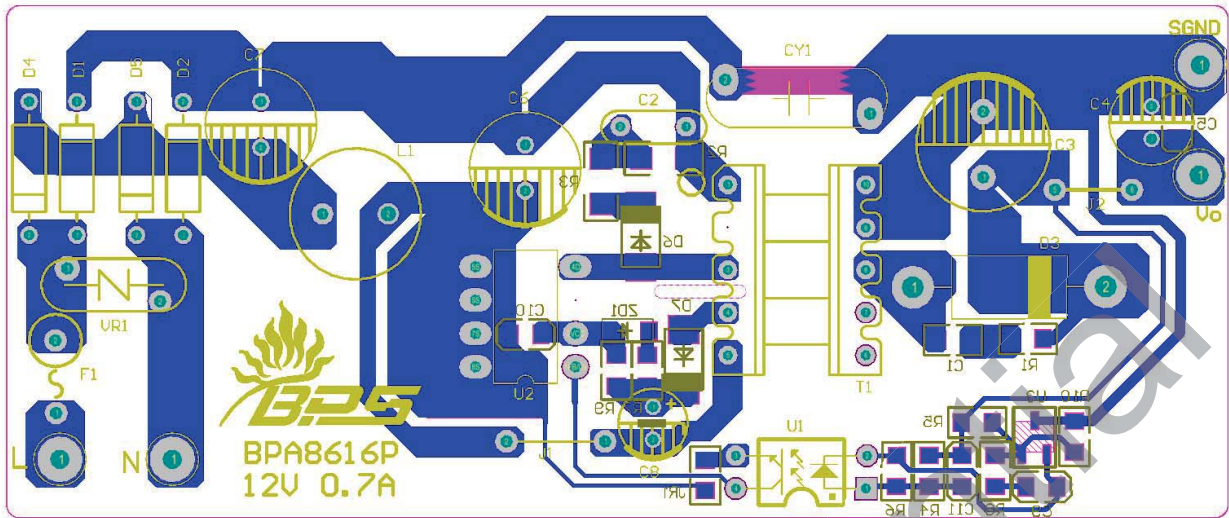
BPA8616P 设计实例 PCB Layout (单面板)
